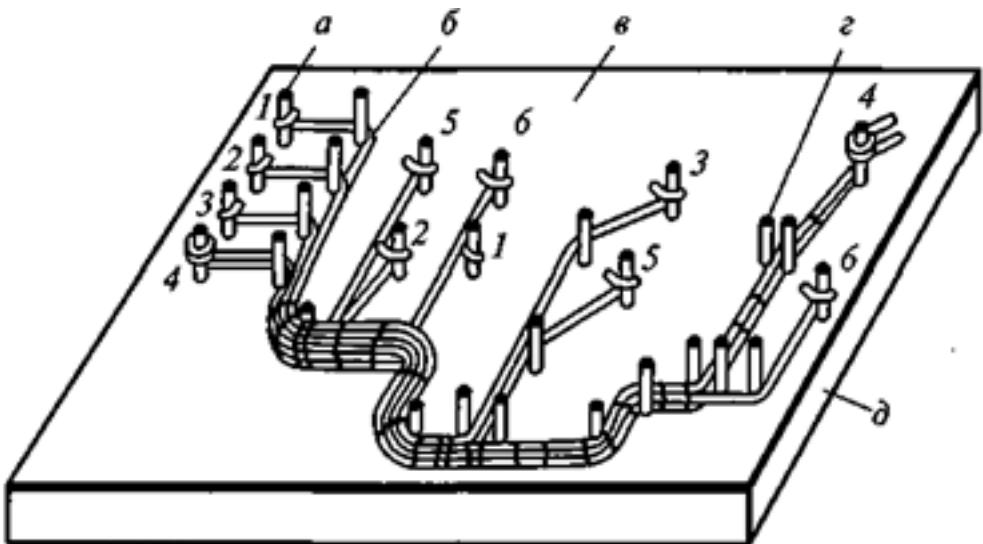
Шаблон для укладки и вязки жгутов:
